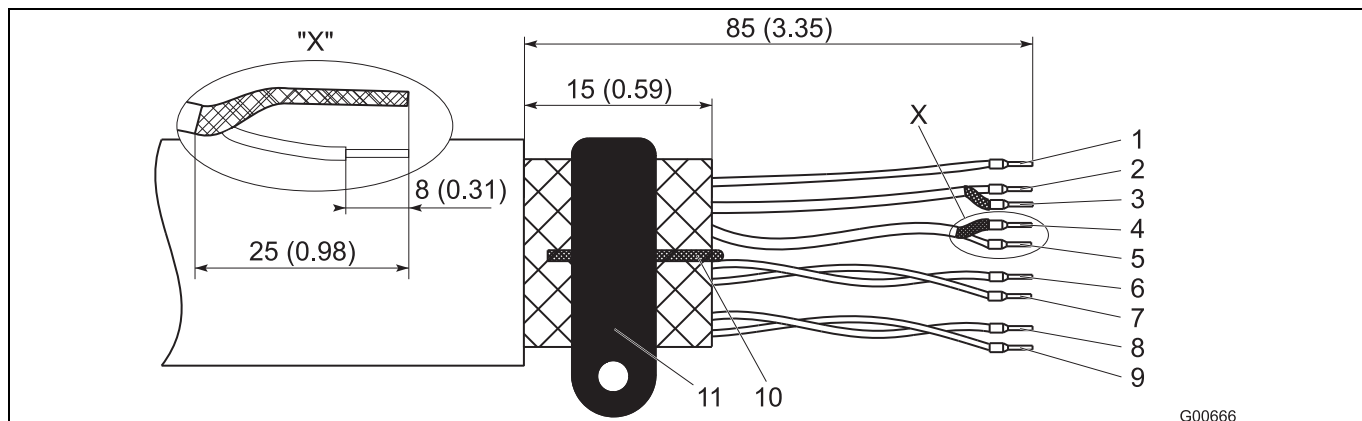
Lado do sensor de medição, dimensões em mm (inch)
